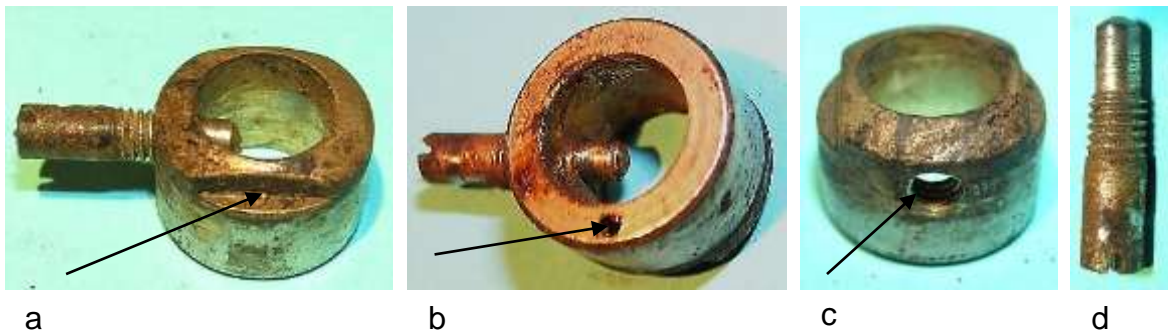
Sperrstiftring: a) Schlüsselseite des Rings, b) Federseite, c) Gewindebohrung für den Sperrstift, d) Sperrstift
